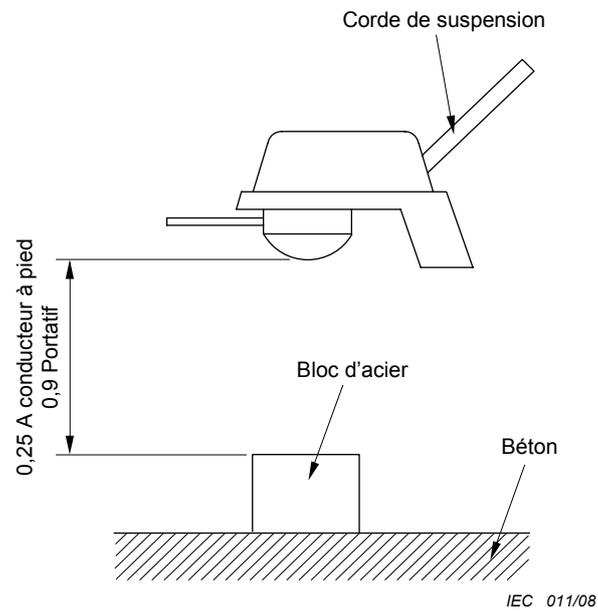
Essai de rigidité de la tête de coupe (voir 21.102)
